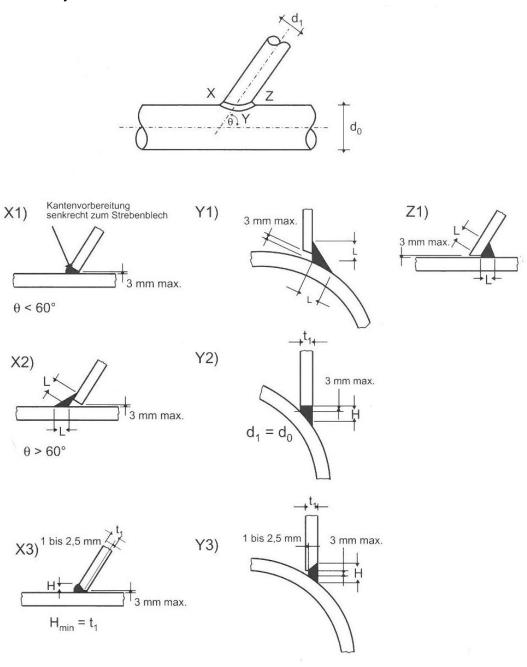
Kehl- und Stupmfnähte in KHP-Anschlüssen nach CIDECT [39] Figure 4-2: fillet and butt welds for KHS-joints according to CIDECT [39]
